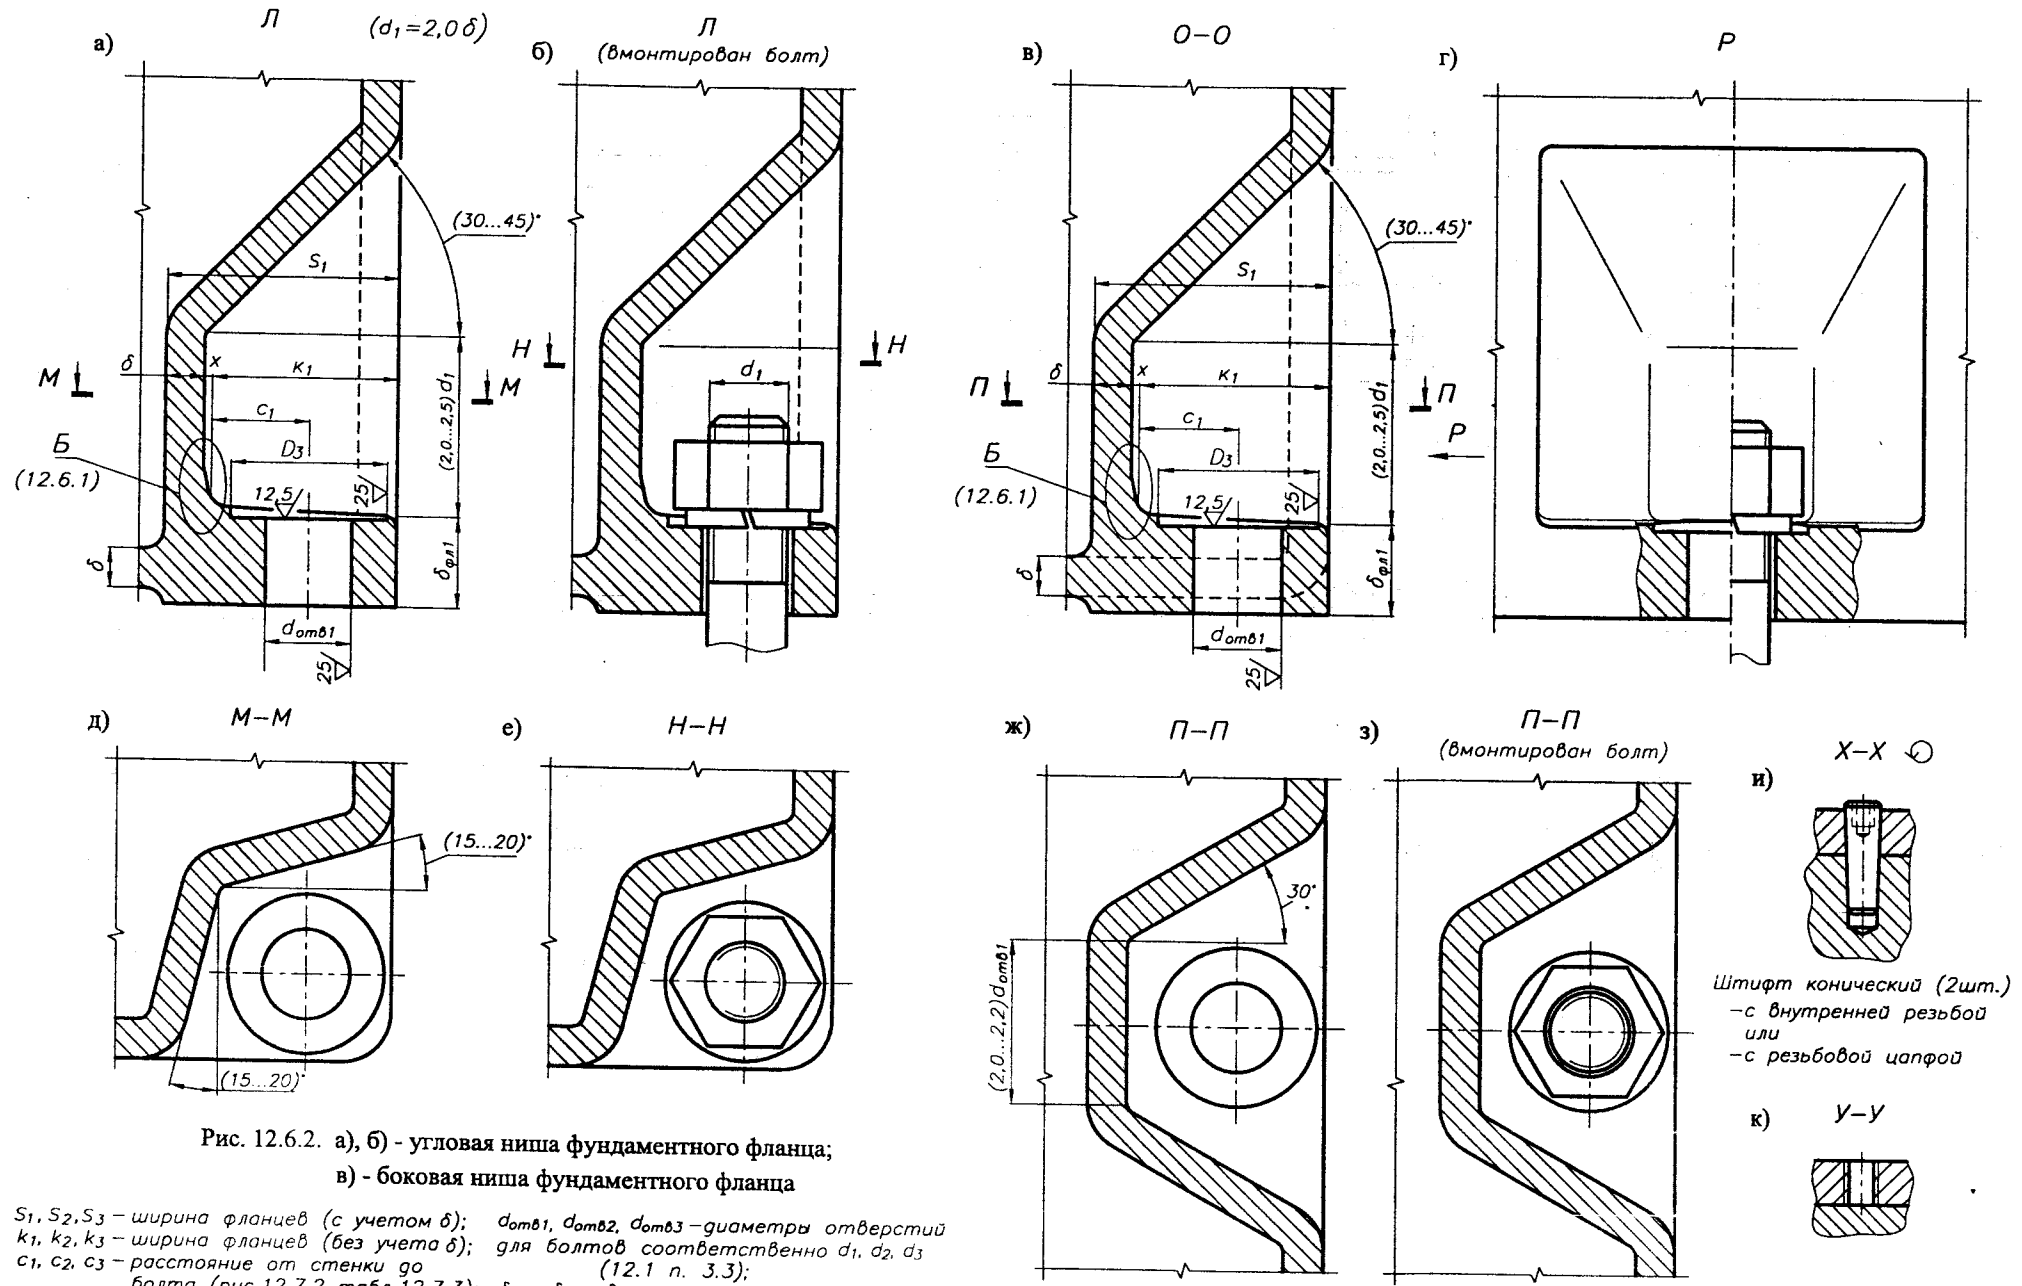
а), б) - угловая ниша фундаментного фланца;
